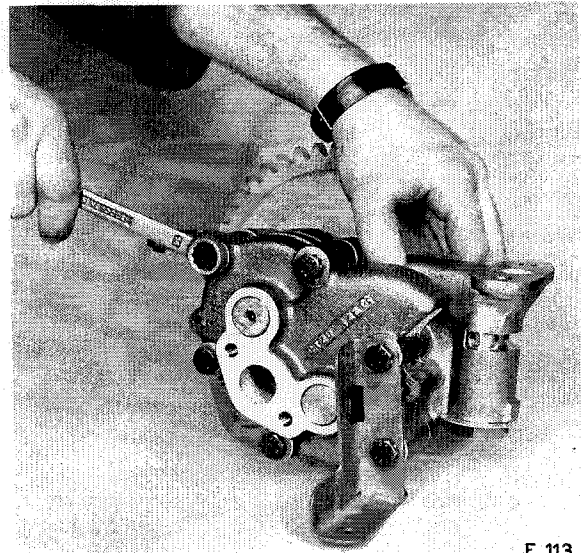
Lösen der Befestigungsschrauben an der Ölpumpe
